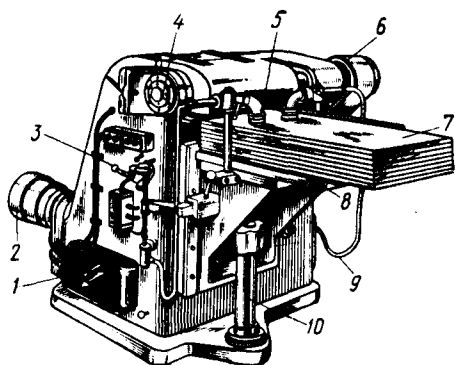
Односторонний ящичный шипорезный станок ШПК-40:
